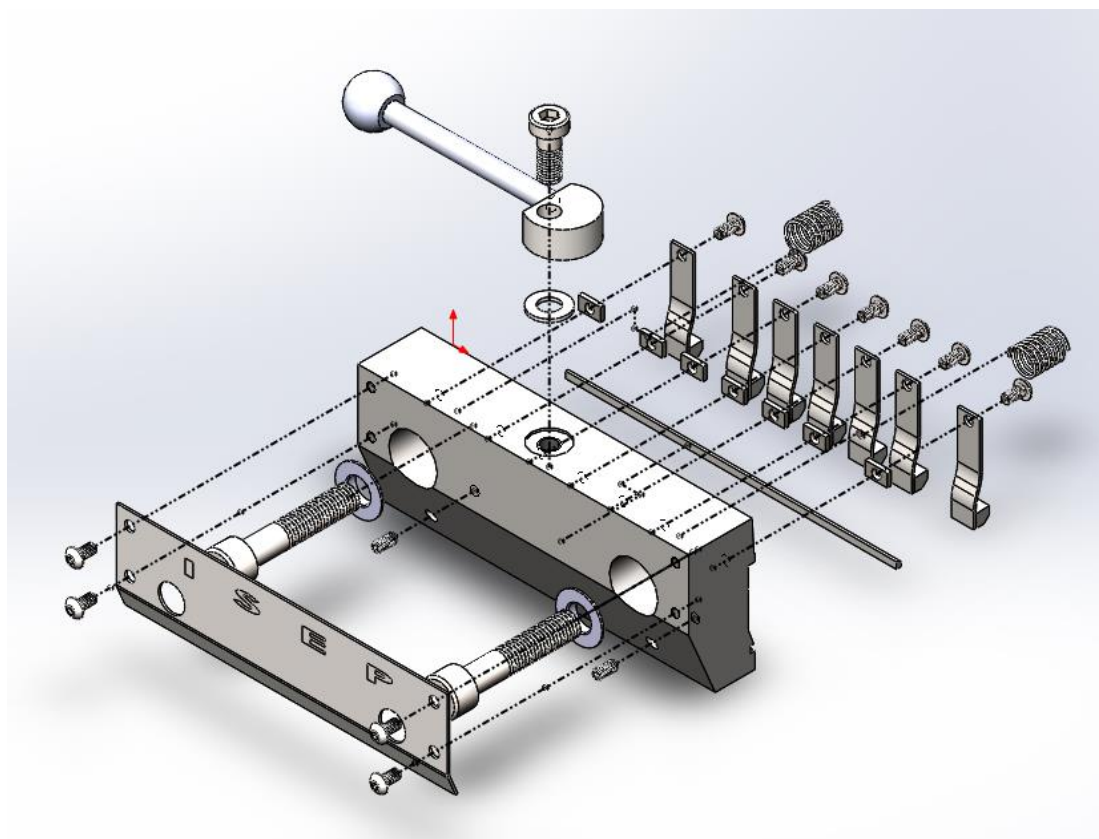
Vista explodida do Suporte_5 - Mola de lâmina
